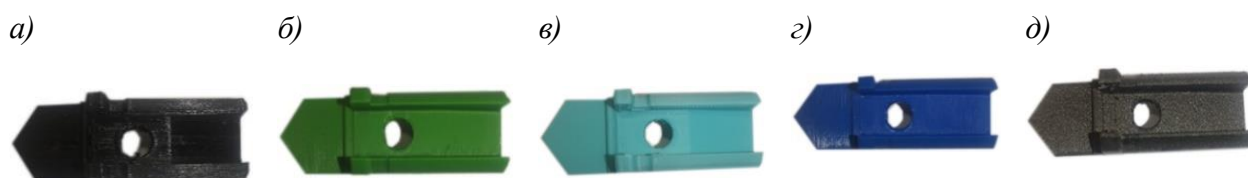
Внешний вид державки блока резцового из различных марок пластиковых материалов: а) – ABS-GF; б) – ABS; в) – PLA; г) – SBS; д) – Pet
